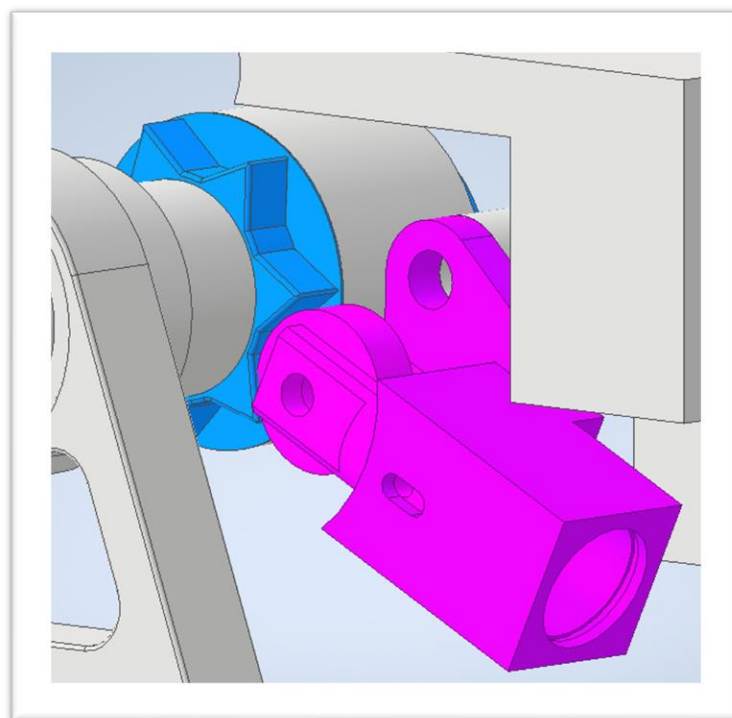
Sistema de fixação do tambor (Fonte: Autor)
